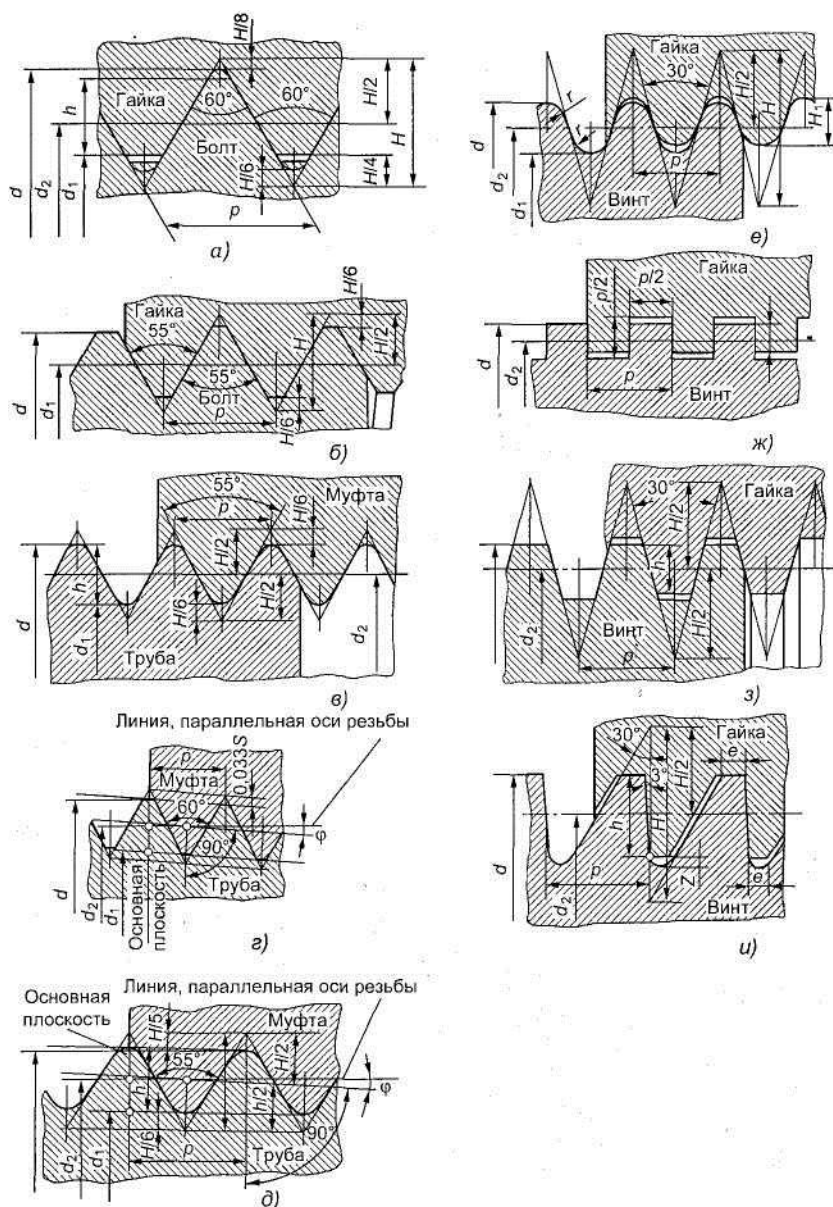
Профили резьб: а — метрическая; б — дюймовая; в — трубная цилиндрическая;
